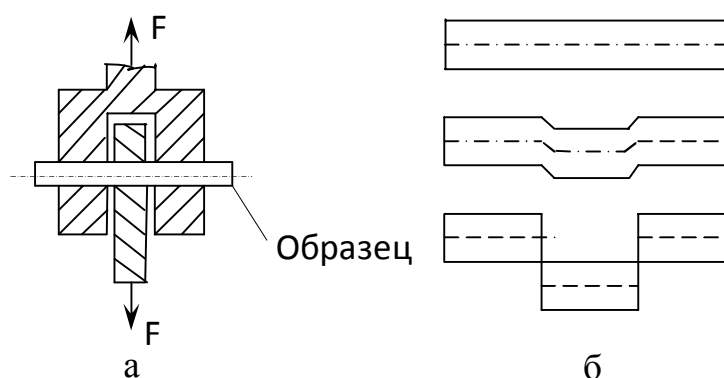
Схема испытания металлических материалов на двойной срез: а – приспособление для испытания образцов; б – деформация и разрушение образца
